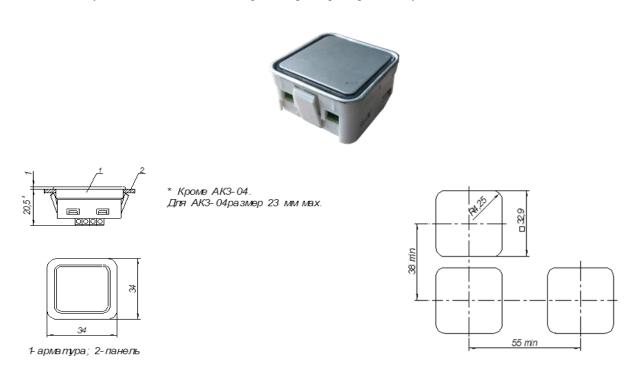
Внешний вид, габаритные размеры и разметка установочных мест для АК3, АК4
